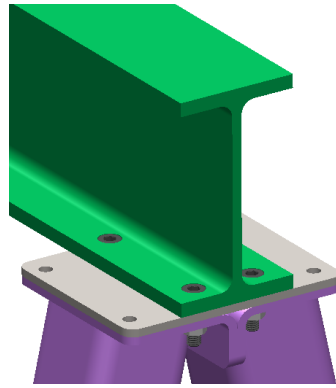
Vista de montaje de pieza N°5 en la parte superior de la estructura (Fuente 91)
